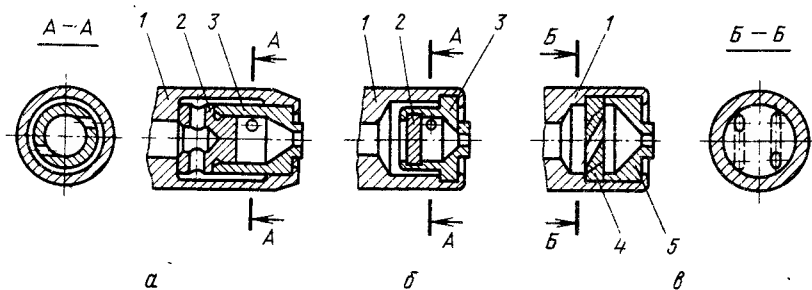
Конструктивные схемы центробежных форсунок:
